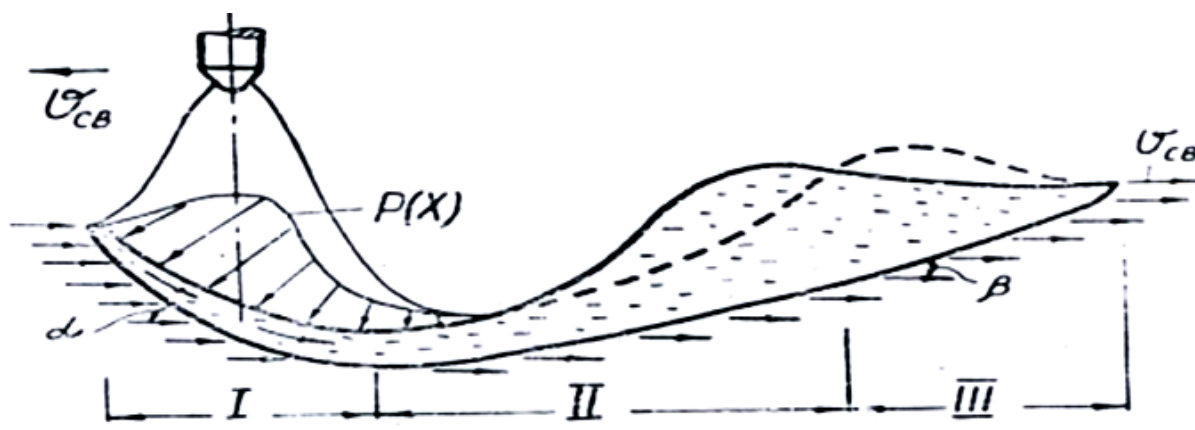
Гидродинамическая модель сварочной ванны
